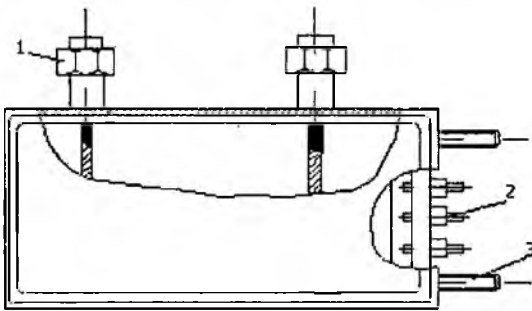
Конструкторсько-технологічний варіант виконання мікроблоку з комбінованим фрезерувально-штамповочним корпусом:
